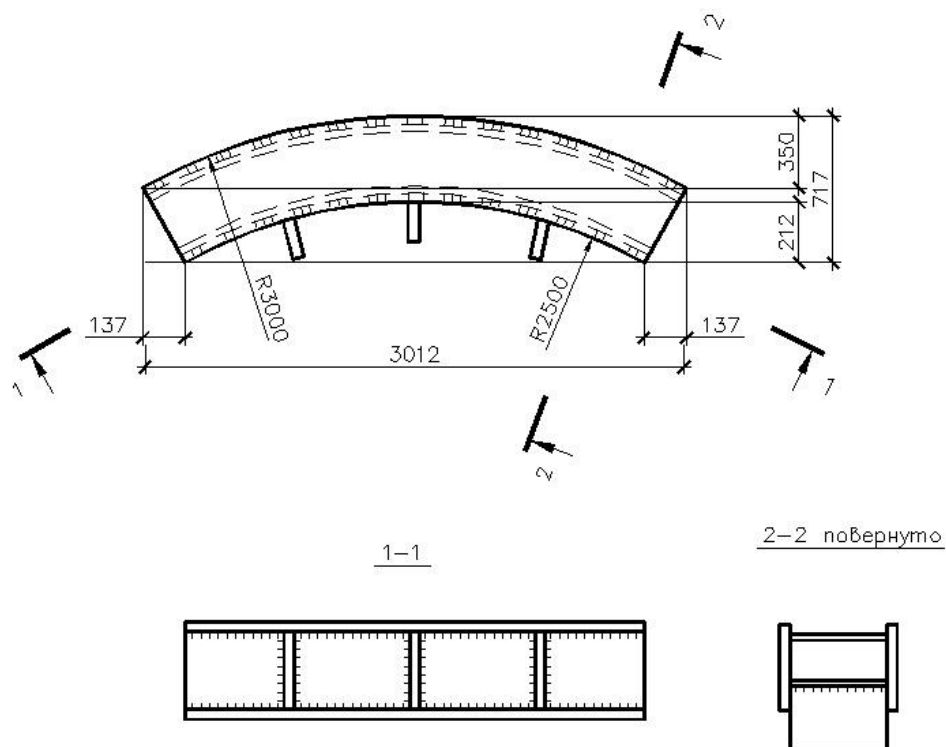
Разрез с секущей цилиндрической поверхностью
